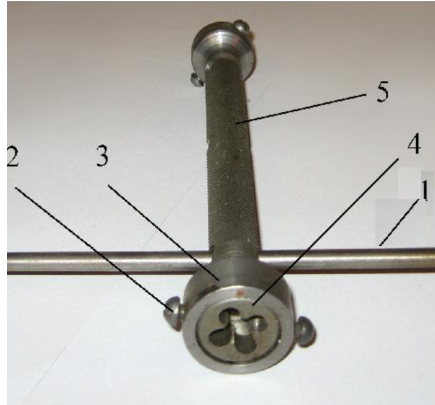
Плашкодержатель для нарізання різьби вручну:
